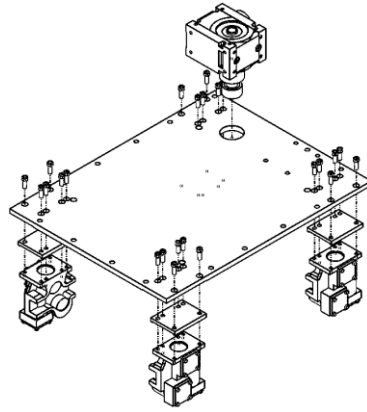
Perspetiva isométrica "Assembly carro para CM Carril".
